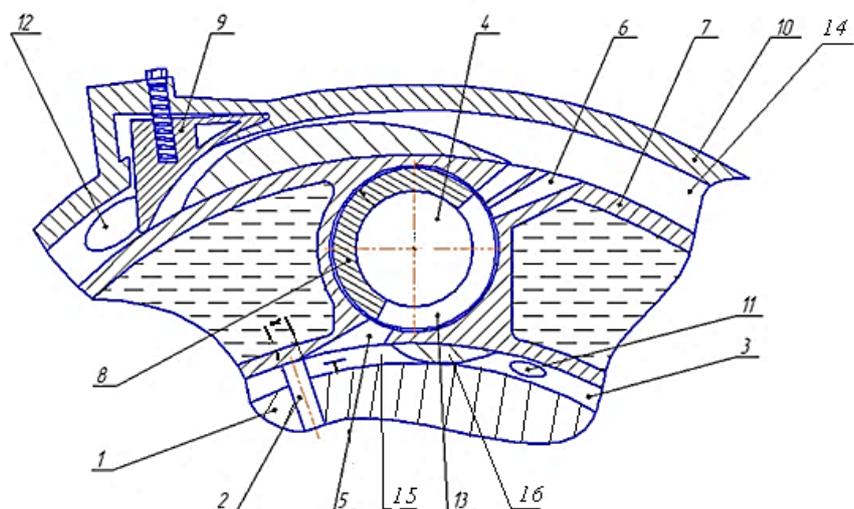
Камера сгорания роторного двигателя: 1 – ротор компрессора, 2 – рабочая заслонка компрессора, 3 – рабочая полость компрессора, 4 – камера сгорания, 5 – перепускной канал, 6 – выпускной канал, 7 – рабочее кольцо, 8 – газораспределительный стакан, 9 – рабочая заслонка турбины, 10 – турбина, 11 – впускной канал, 12 – выпускной канал, 13 – окно газораспределительного стакана, 14 – рабочая полость турбины, 15 – камера сжатия, 16 – уплотняющий выступ
